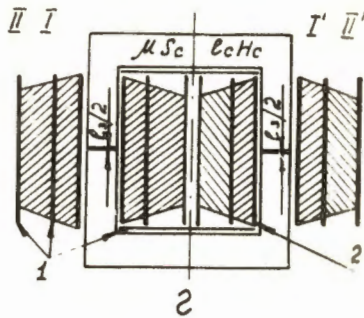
Эскиз конструкции повышающего резонансного трансформатора блока ВВП-30К.
